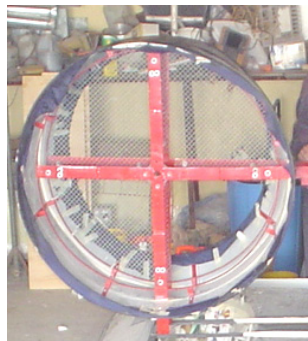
Tobera cubierta con fibra de vidrio y recubiertas con tela poliéster.
